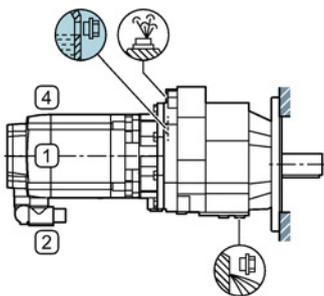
Einbautagen für Stirnradgetriebe DF und ZF (Flansch-) oder DZ und ZZ (Gehäuseflanschausführung), Baugröße 39, 2-stufig und 3-stufig
